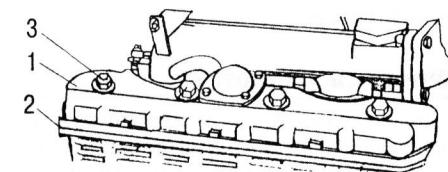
Снятие колпака крышки головки блока цилиндров: 1 – колпак крышки; 2 – прокладка; 3 – гайка колпака
